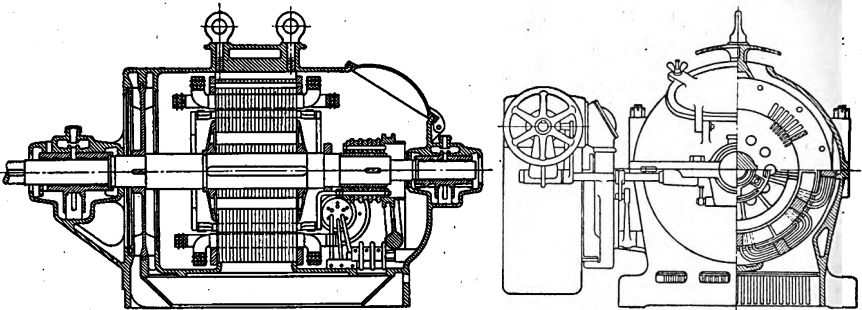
Gekapselter Asynchronmotor der Siemens-Schuckertwerke, Berlin, mit angebautem Anlasser und Umlaufkühlung.
